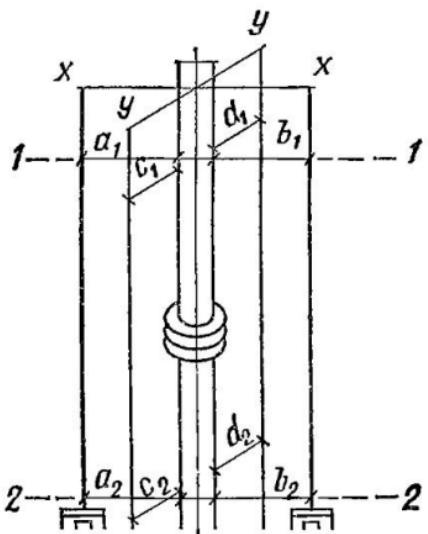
Выверка вертикального вала агрегата с помощью четырех струн
